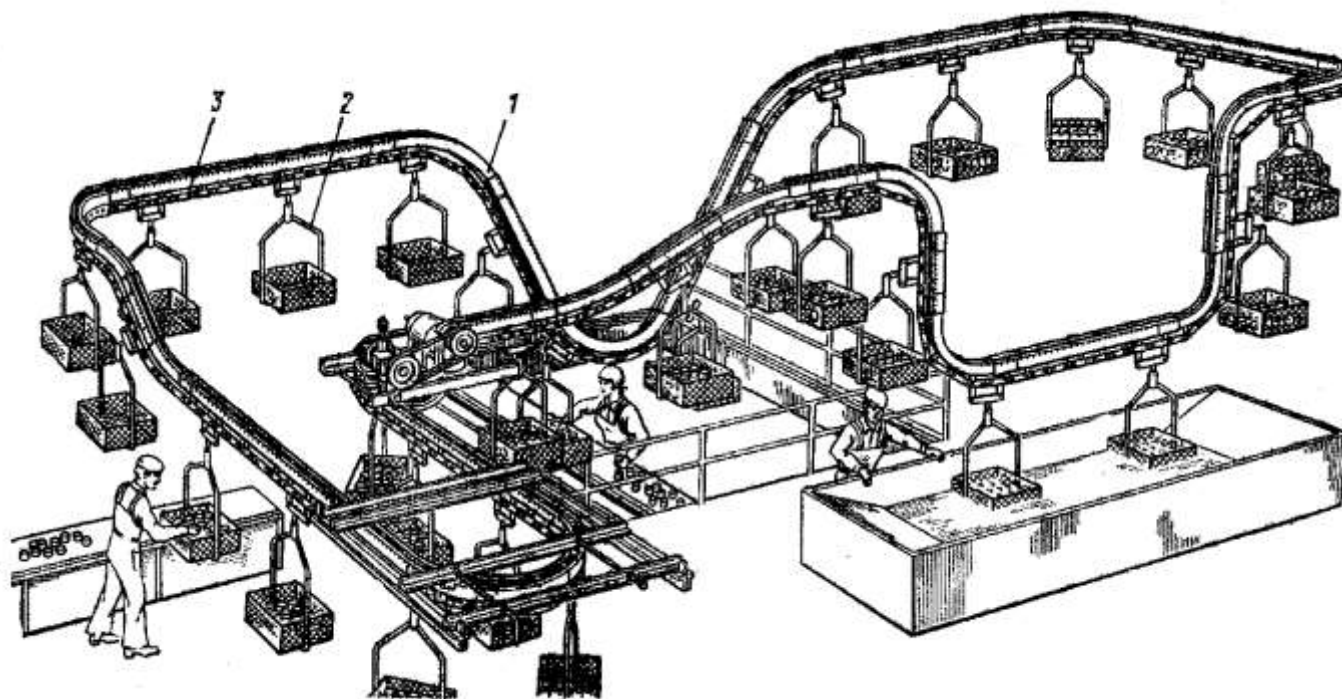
общий вид грузонесущего подвешного конвейера
